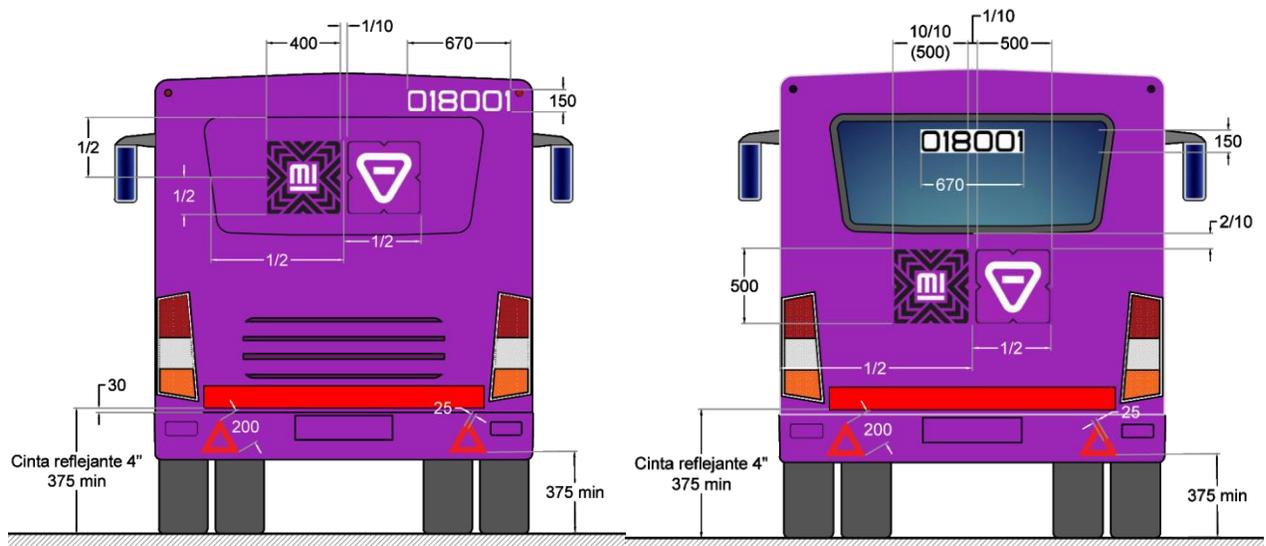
Alzado posterior, cromática autobús piso bajo con y sin medallón.
